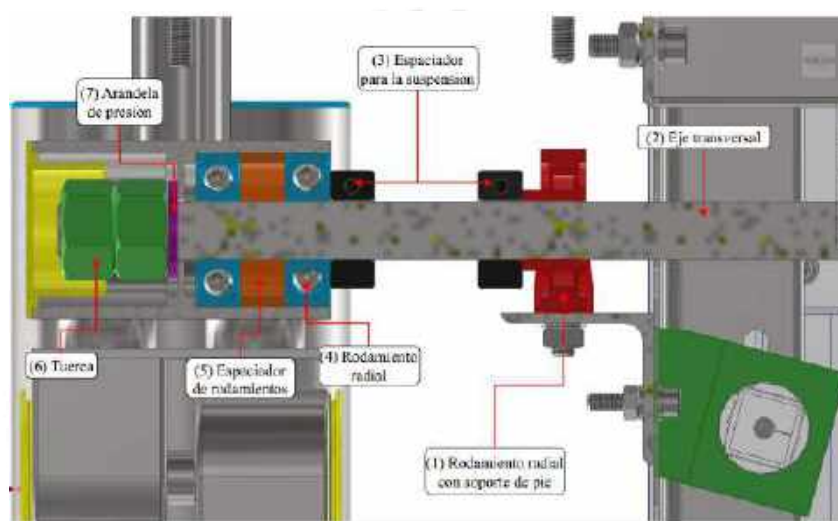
Acoplamiento de la suspensión Rocker-Bogie y la jaula soldada.
